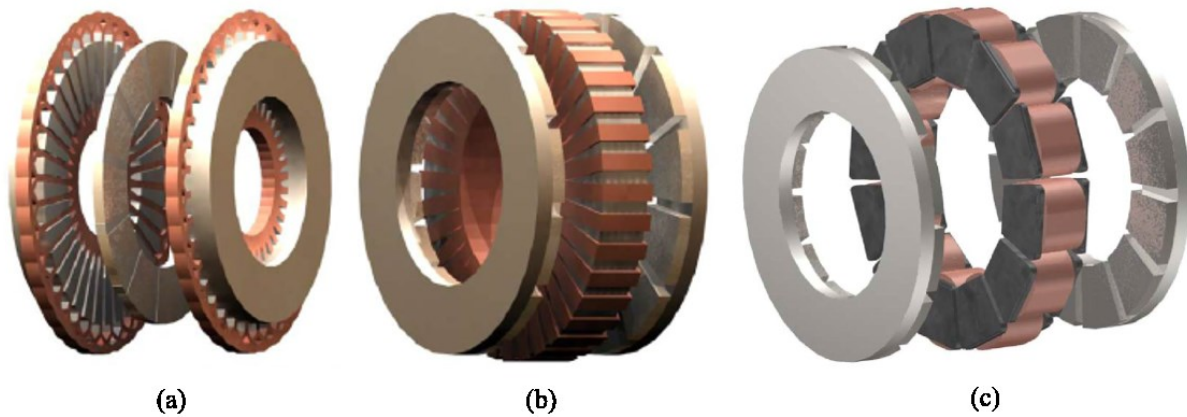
Machines à flux axial à rotor interne (a), de type TORUS (b) et de type YASA (c) [9]
